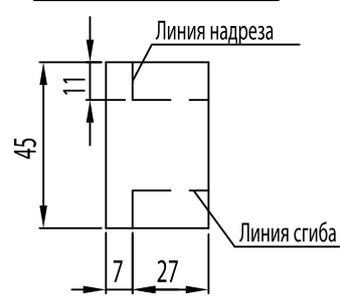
Тепловая изоляция фланцевой арматуры
